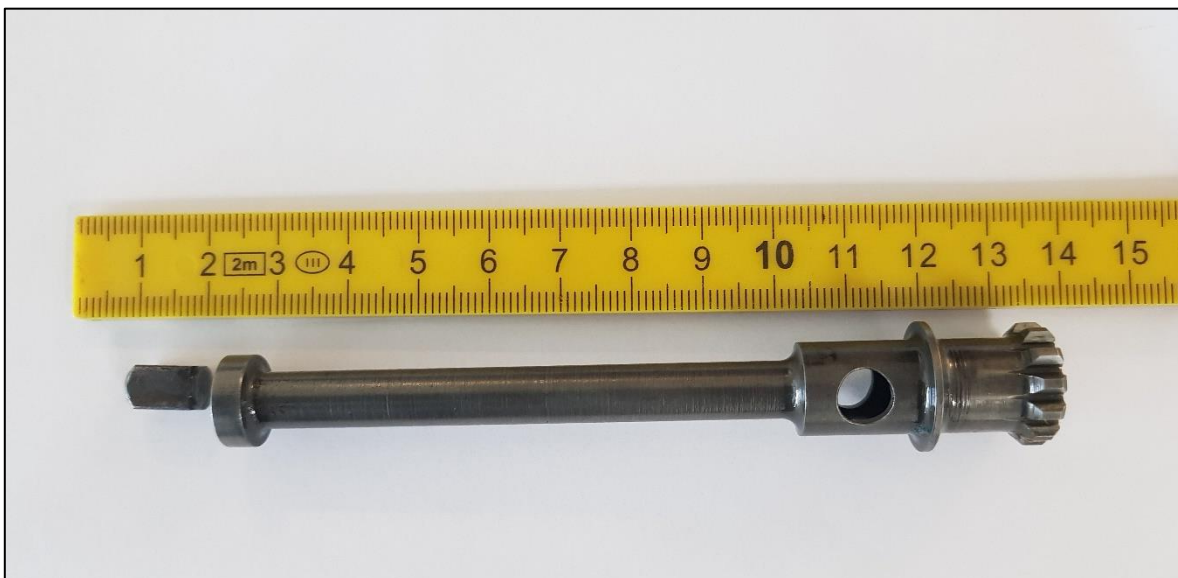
Bomba de combustible y eje (Shaft-Fuel Pump Drive)
